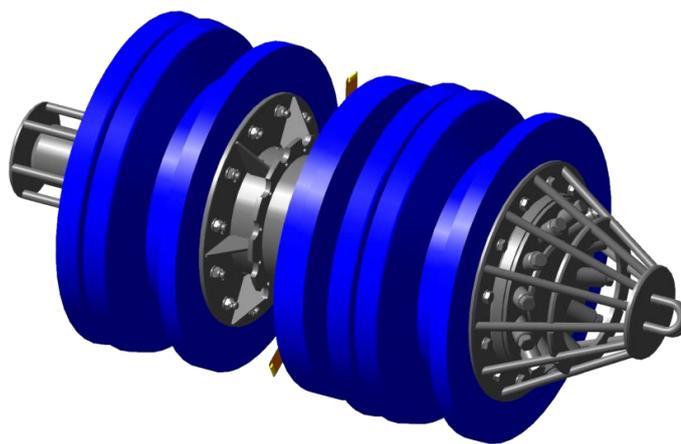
Поршень-разделитель типа ПРВ1
